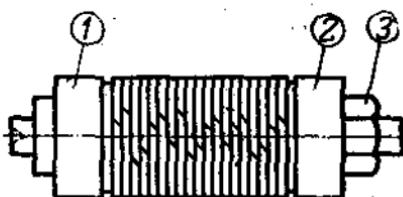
Приспособление для вторичной обточки поршневых колец.
